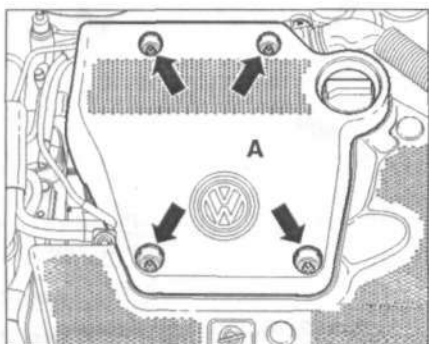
Открутите крепежные гайки (стрелки) и снимите крышку А двигателя.
